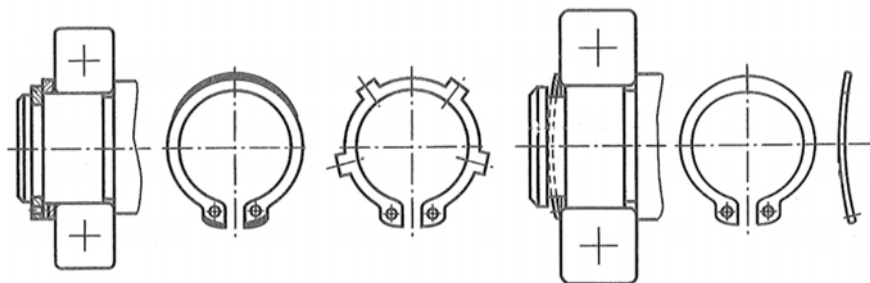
Варианты конструкций крепления внутреннего кольца подшипника к валу в плавающей опоре с помощью пружинных колец
